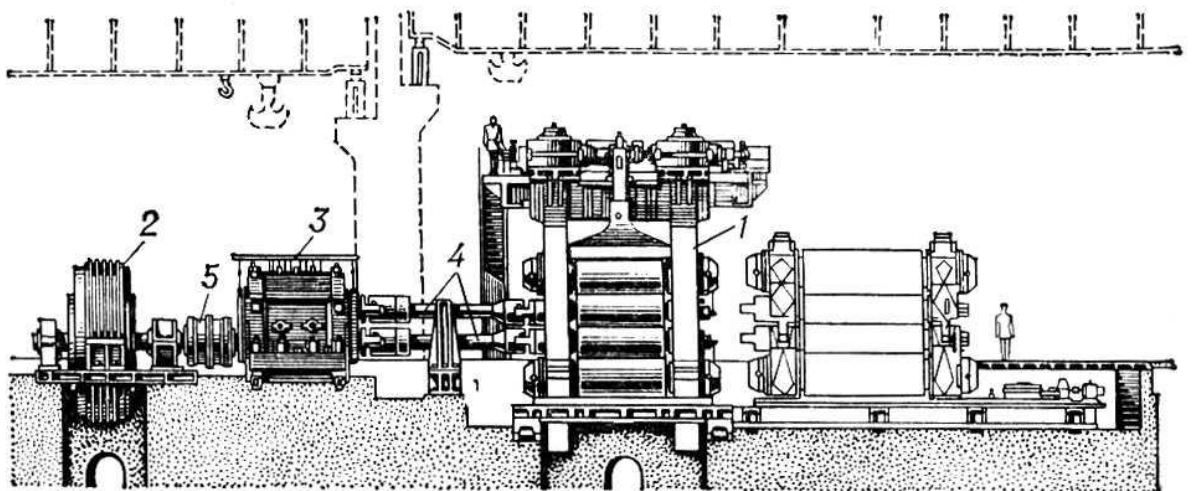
Главная линия непрерывно-заготовочного стана: 1 — рабочая клетка; 2 — электродвигатель; 3 — шестеренная клетка; 4 — шпиндель; 5 — муфта.
